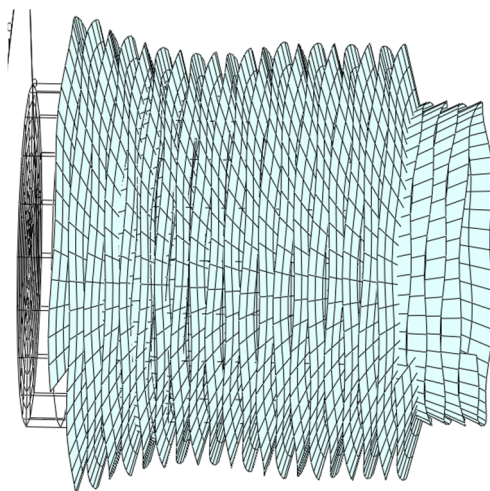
Поверхность резания при точении заготовки с криволинейной образующей
